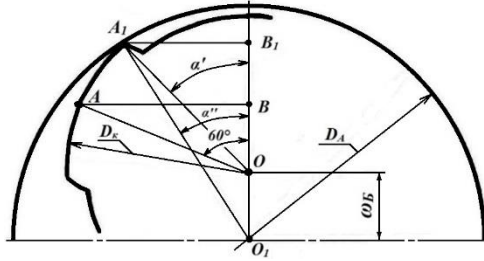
Схема базирования детали на установочно-разжимной оправке
